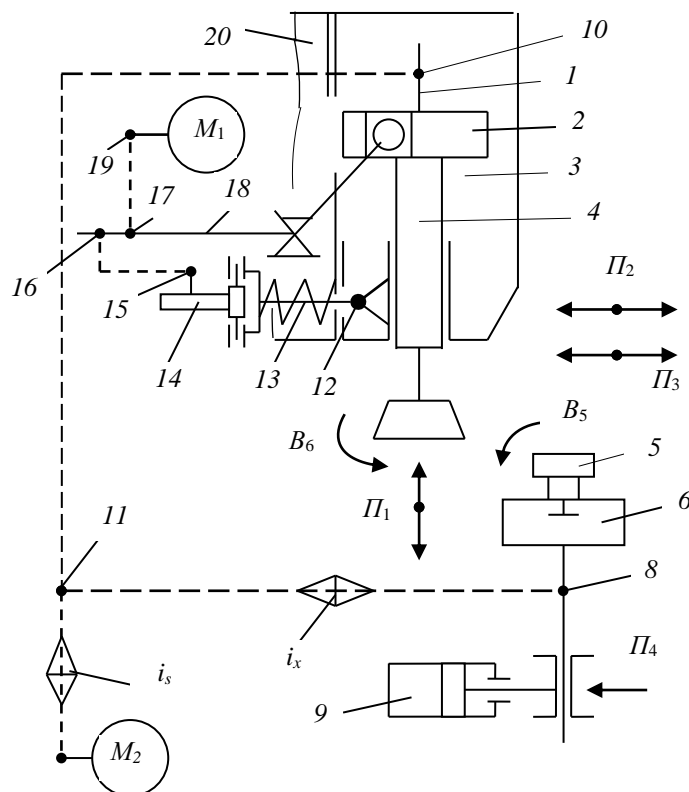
Кинематическая структура зубодолбежного станка для обработки колес с наклонными зубьями
